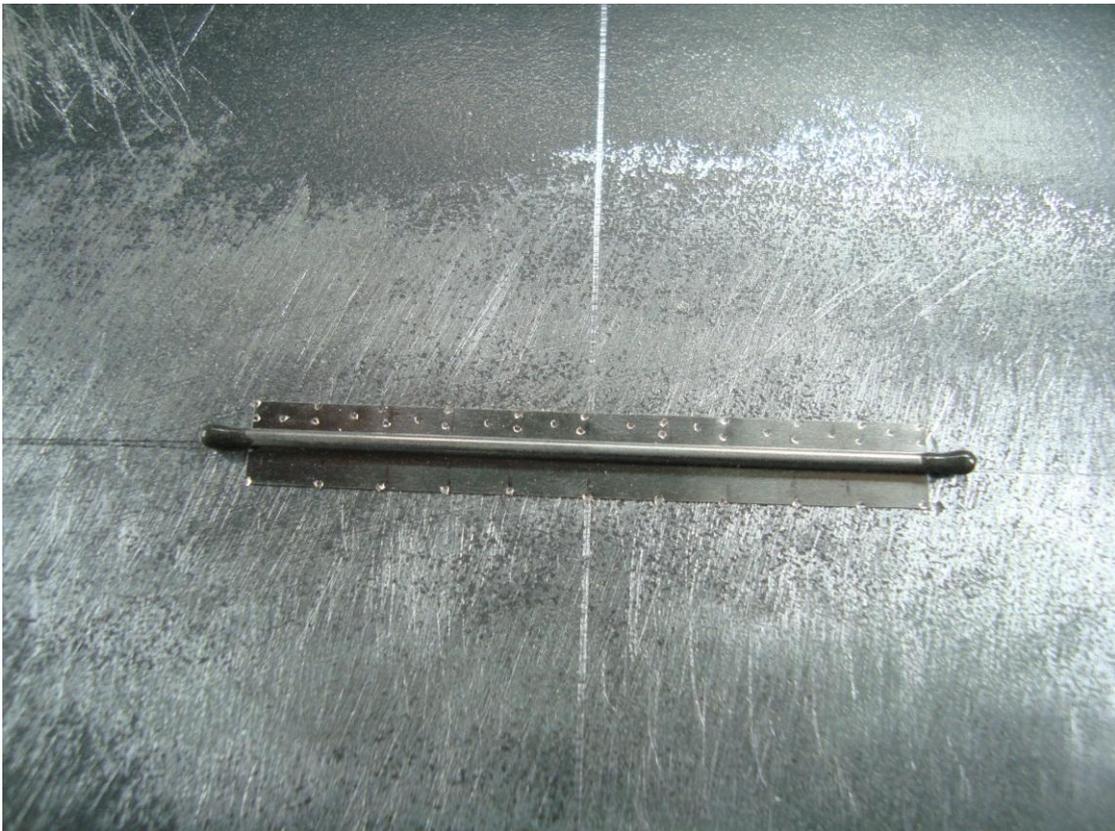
Esquema de colocación de puntos de soldadura
